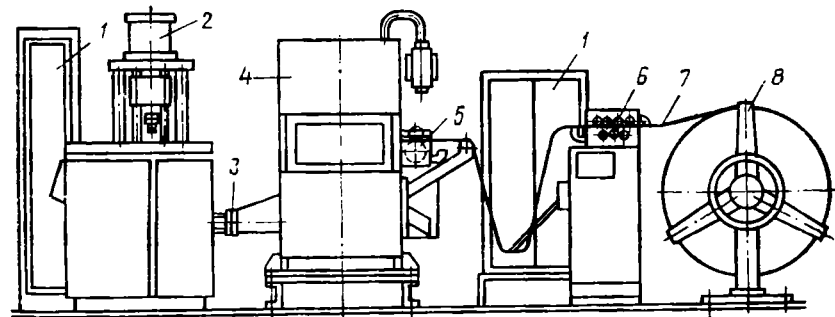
Автоматическая линия штамповки, сборки и скрепления сердечников:
